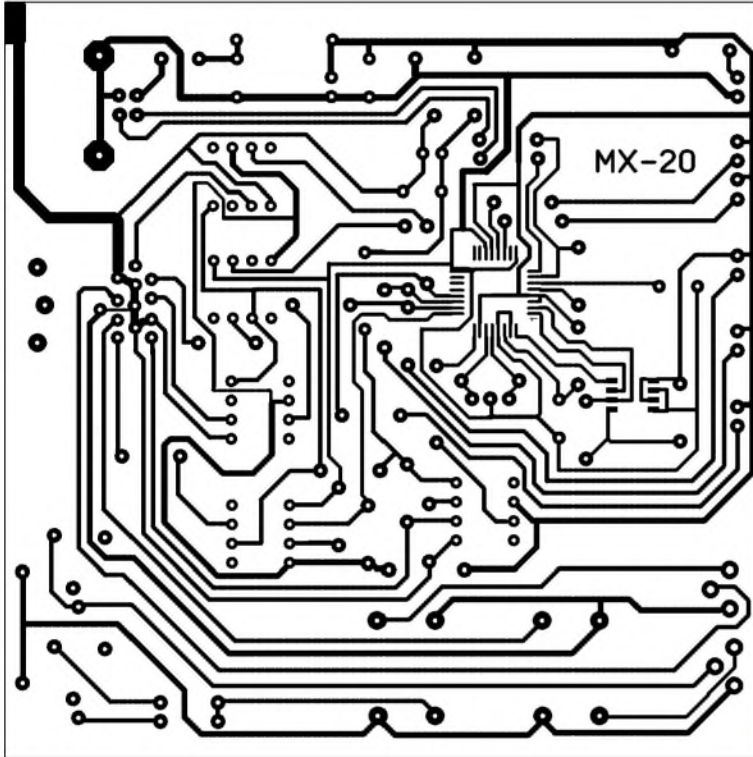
Layout der einseitigen Leiterplatte MX-20, Maßstab 1:1
